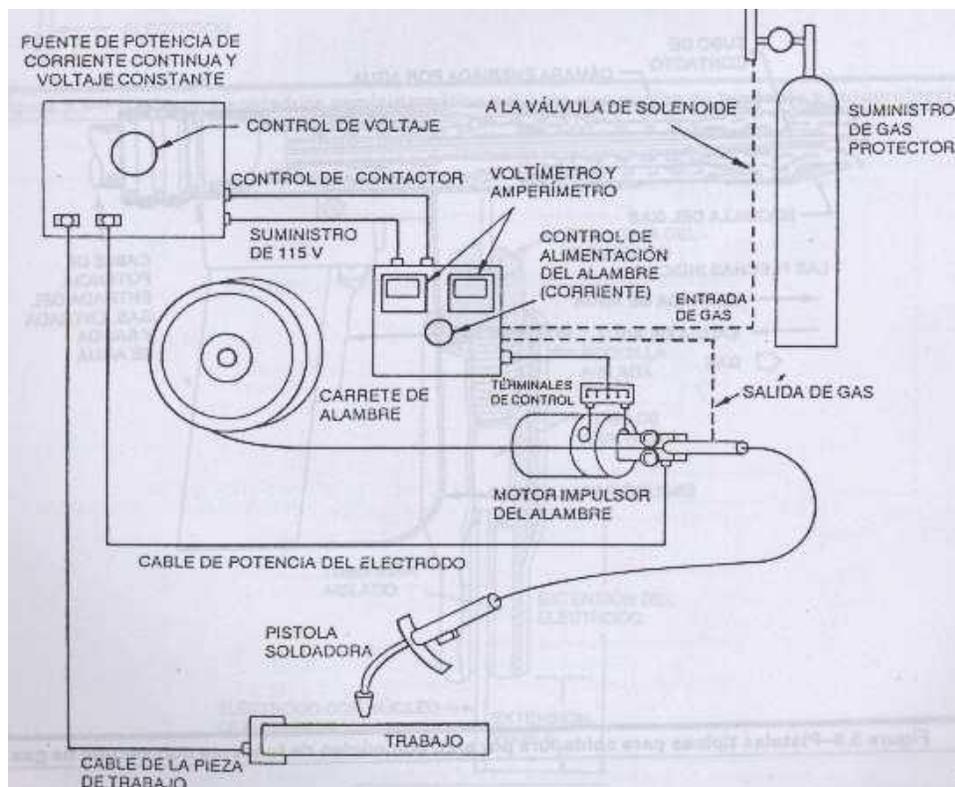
Equipo típico para soldadura FCAW²⁰
